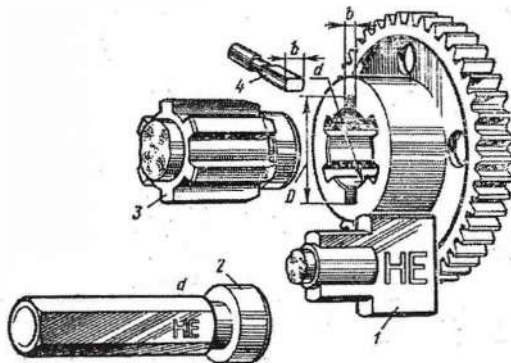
Калибры для контроля шлицевого прямобочного отверстия: 1 — неполный непроходной калибр-пробка для контроля  $D$ ; 2 — поэлементный полный непроходной калибр-пробка для контроля  $d$ ; 3 — комплексный проходной калибр-пробка; 4 — поэлементный непроходной калибр-пробка для контроля ширины паза  $b$  [10, с. 185]
